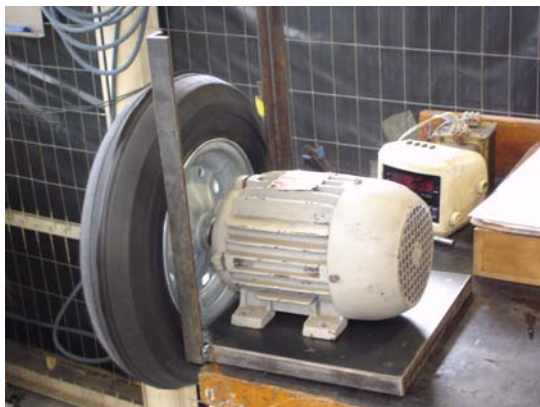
Roda já fixada, com auxílio do parafuso e pontos de solda.
